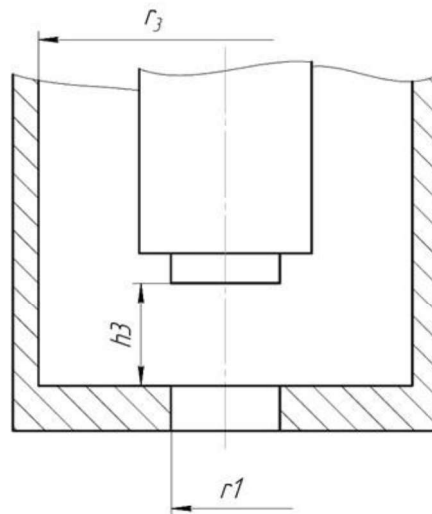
Розрахункова схема дозувально-фасувального пристрою із каналом циліндричної форми
